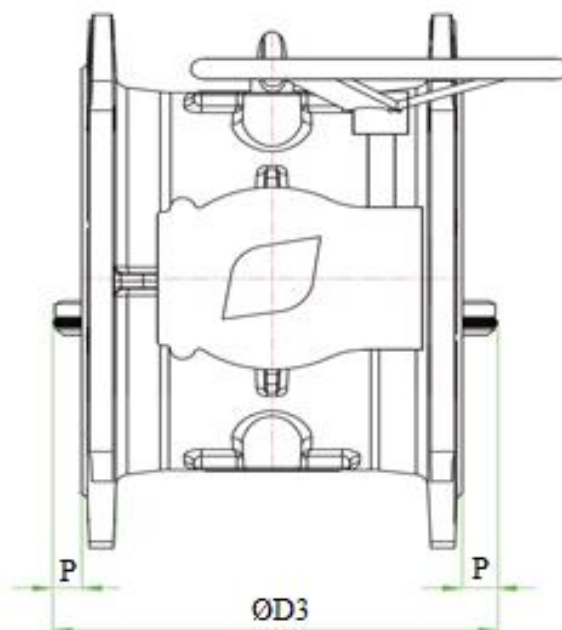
Размеры диска затвора DN200-1600 PN10, PN16
